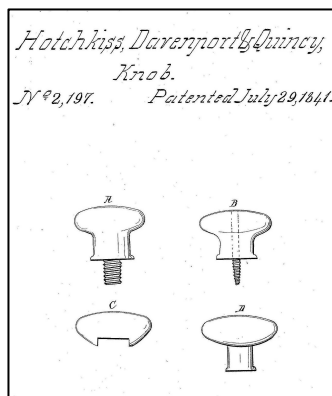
POIGNEES DE PORTE PAR HOTCHKISS (PATENT N° 2197, 29 JUILLET 1841)
